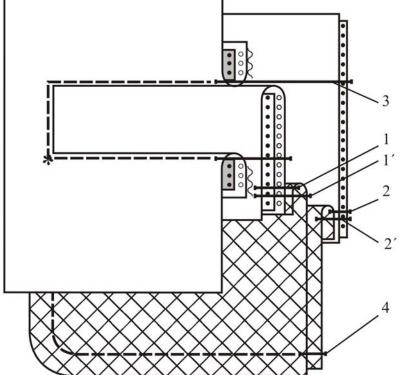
Сборочная схема обработки прорезного кармана с листочкой
